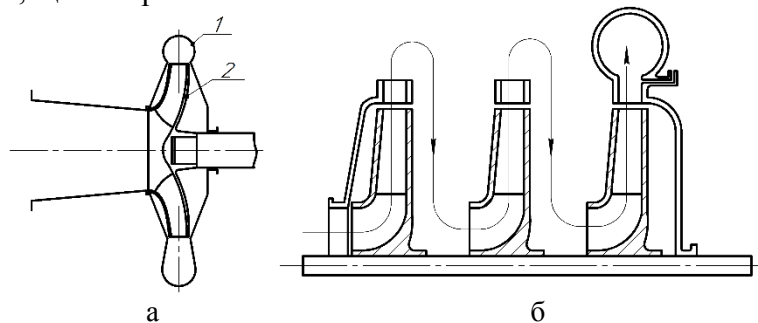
Схеми лопатевих насосів: 1 – корпус;
